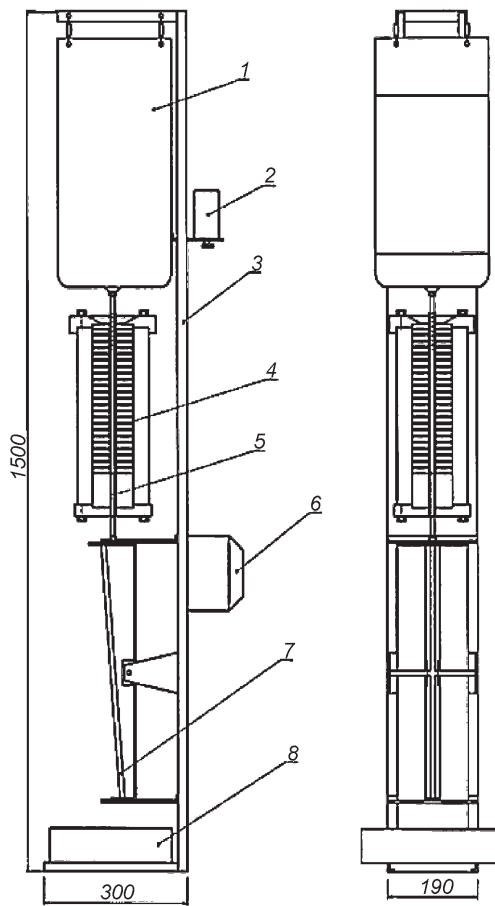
Схема автоматического устройства: 1 — бункер; 2 — вибратор; 3 — рама; 4 — индуктор; 5 — изолирующая трубка; 6 — электромагнитный толкатель; 7 — дозатор; 8 — емкость для обработанных шариков
